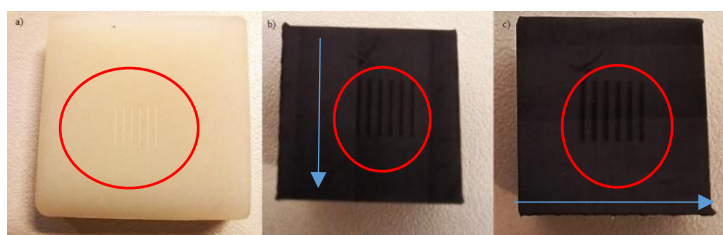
Corpos-de-prova: a) PA66/6, b) PA66/6-BM-PERPENDICULAR e c) PA66/6-BM-PARALELO
